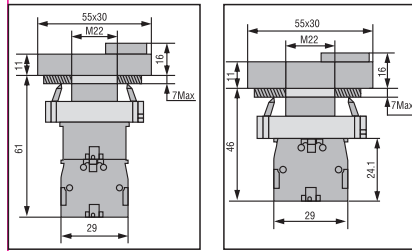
Габаритные и установочные размеры устройств PE-22-PPBB
